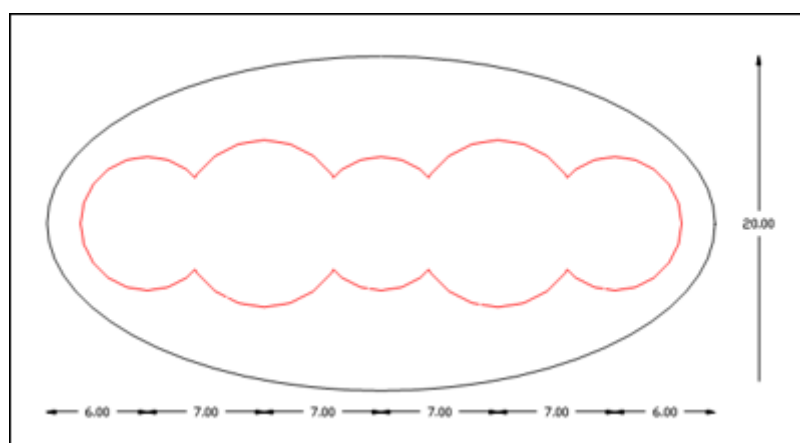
Geometria e dimensioni della sezione ellittica
